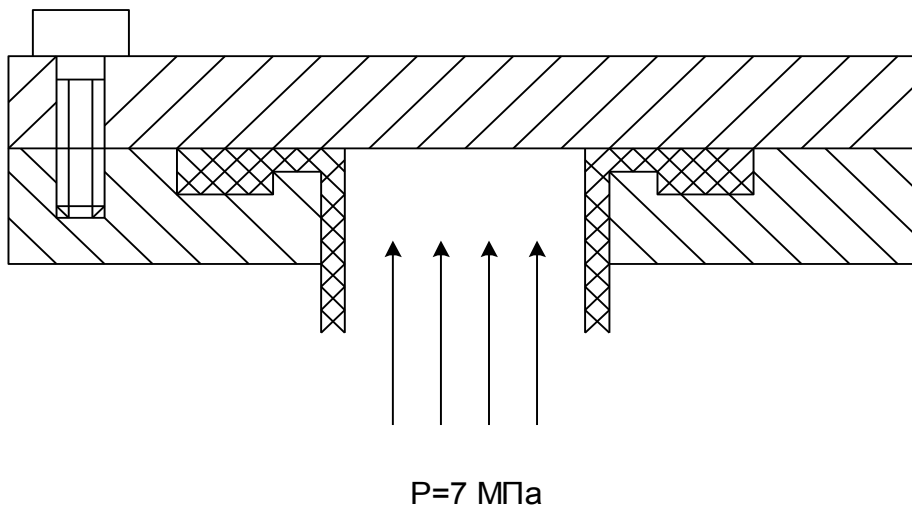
Схема верхней присоединительной части домкрата
